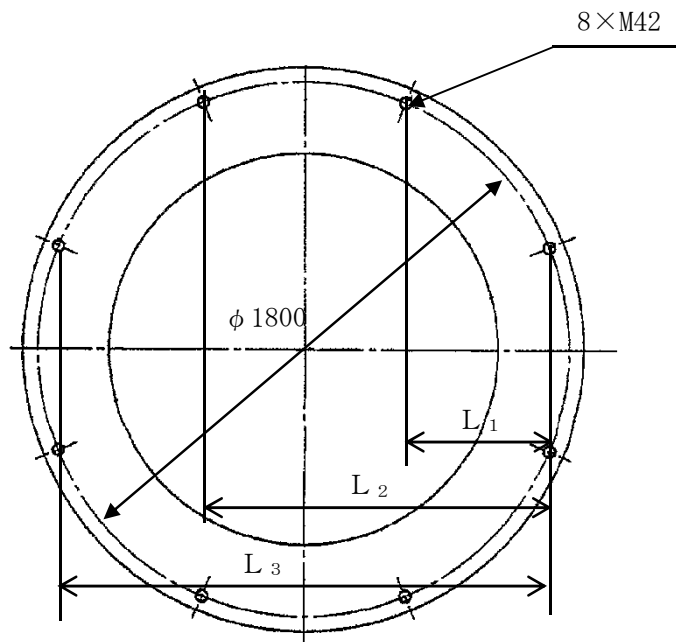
原動機取付ボルトの各ボルト間寸法の配置図
